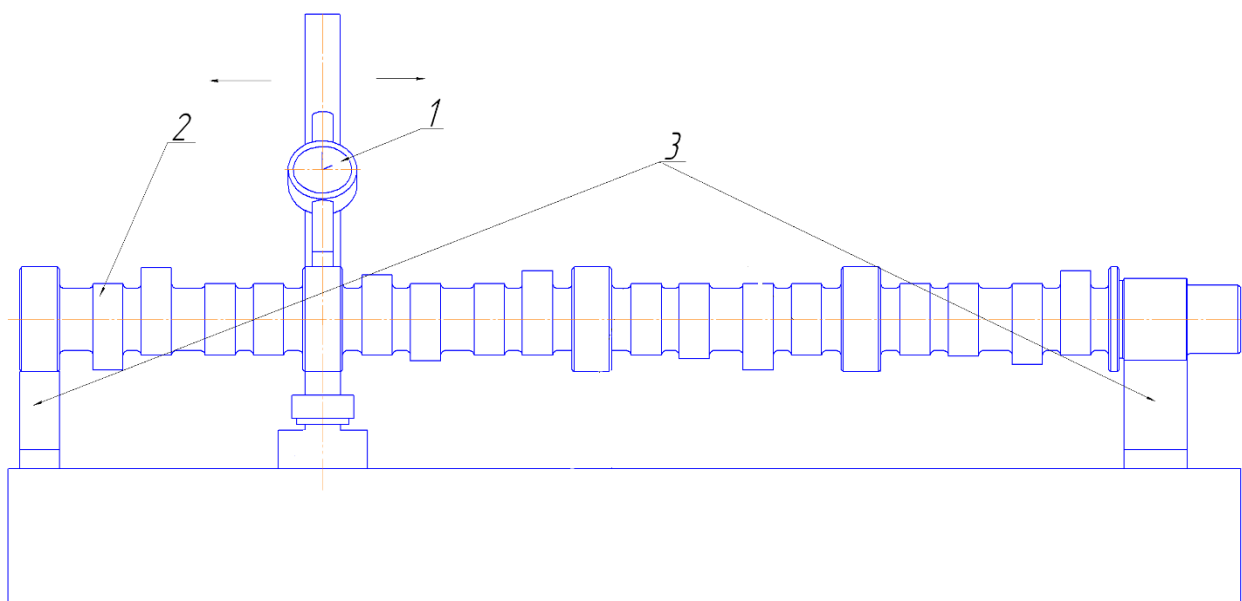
Контрольно-измерительный прибор: 1-часовой индикатор; 2- распределительный вал; 3- призмы опорные.
